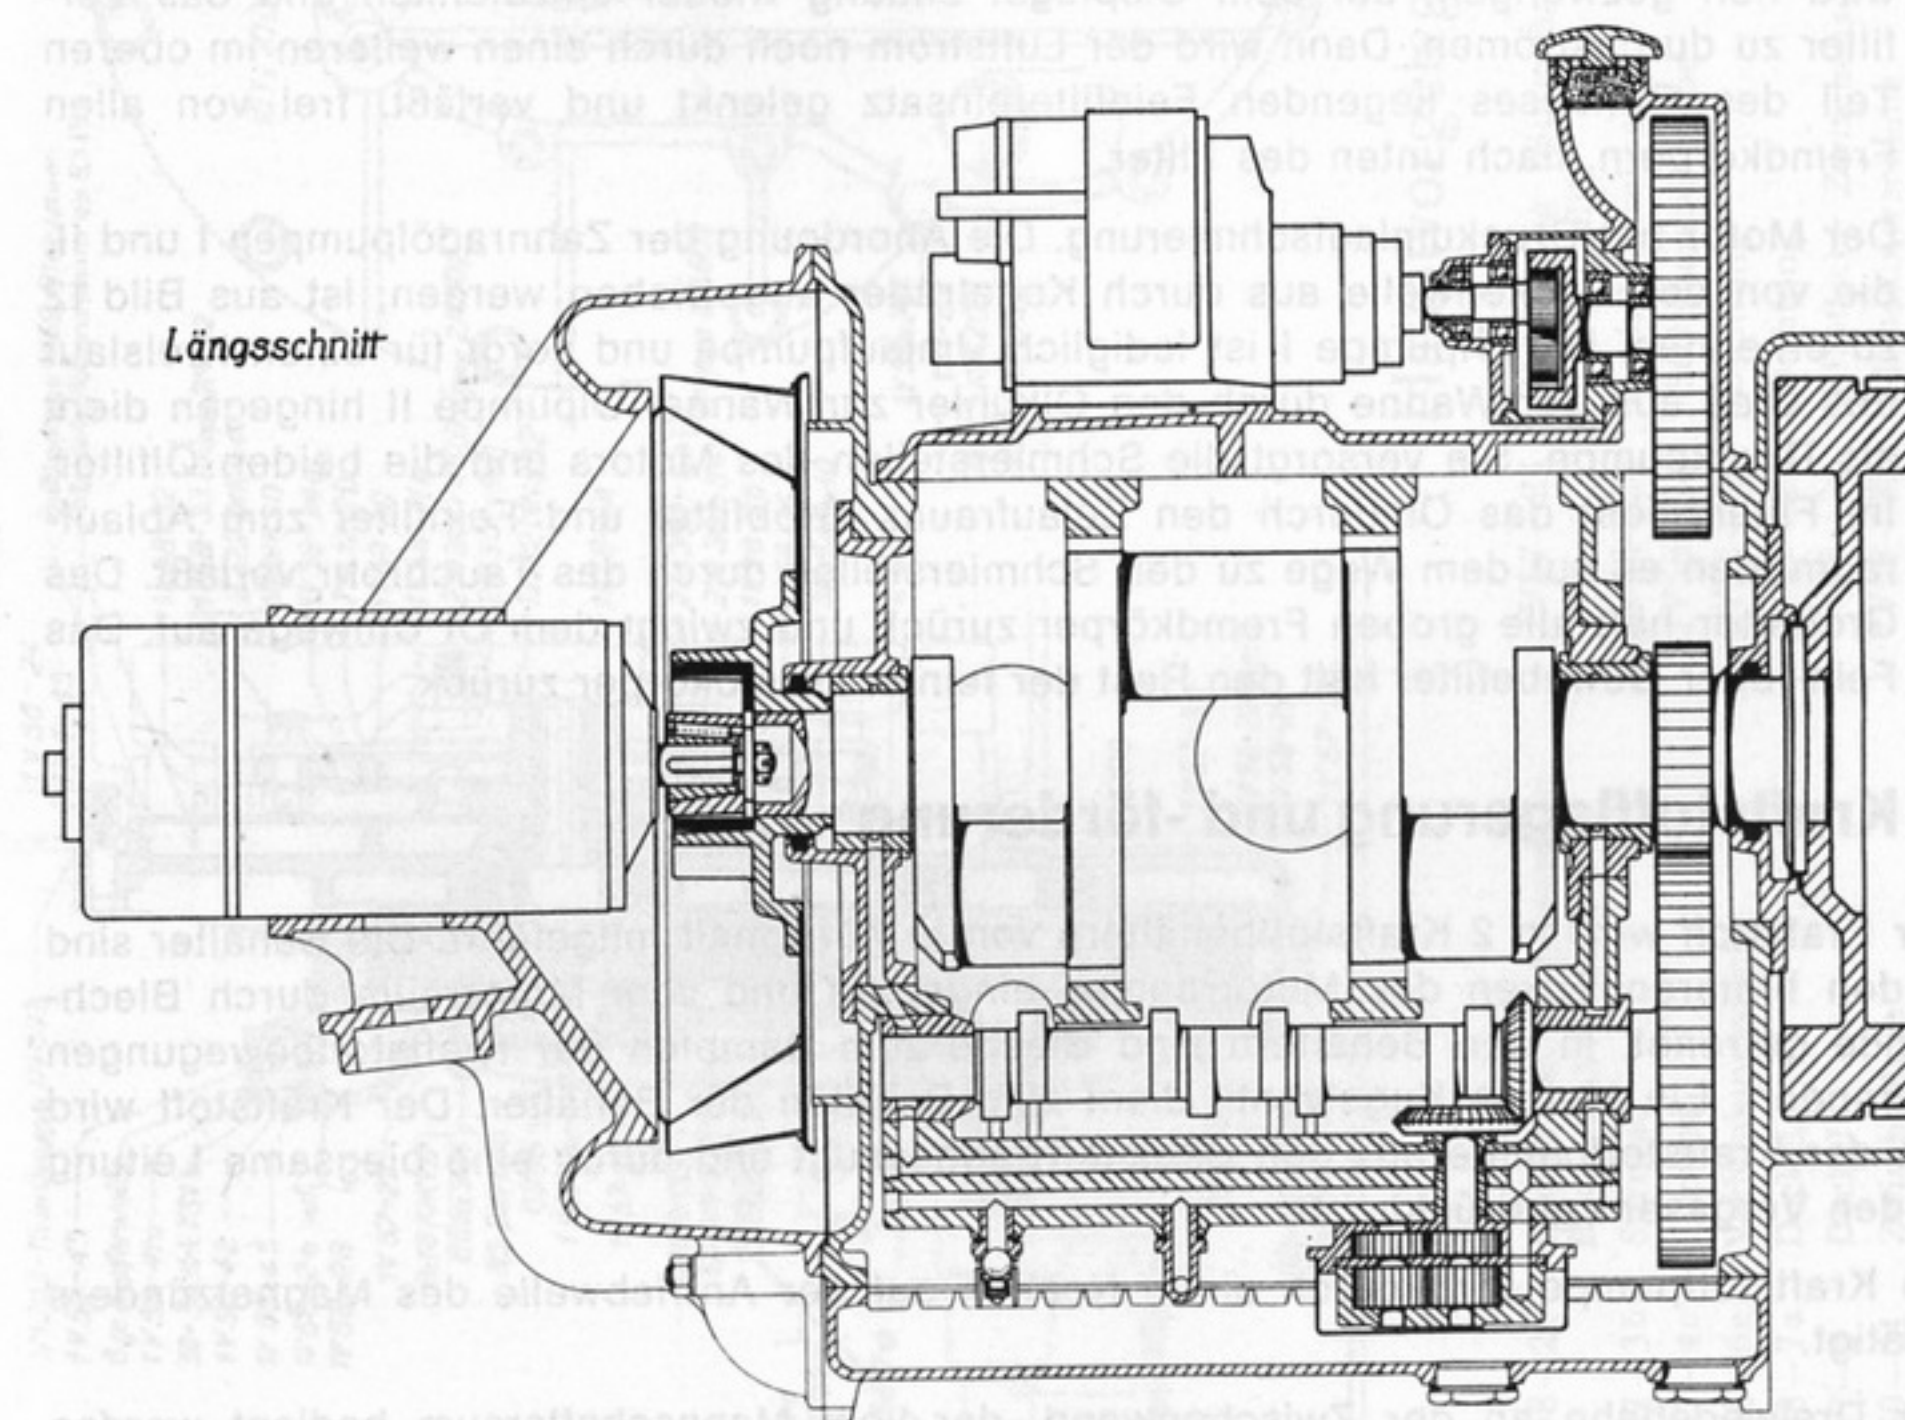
Luftgekühlter 4-Zylinder-Krupp-Motor
